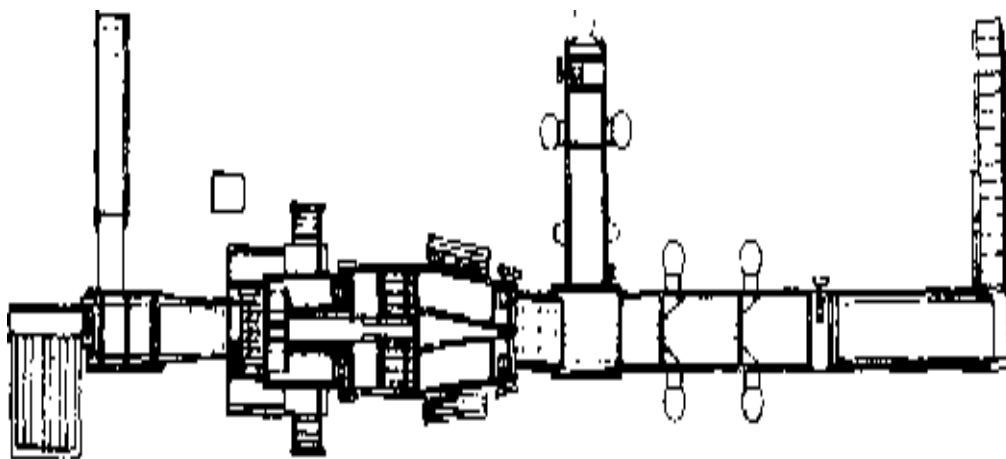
Линия для послеуборочной обработки лука-репки ЛДЛ-10
